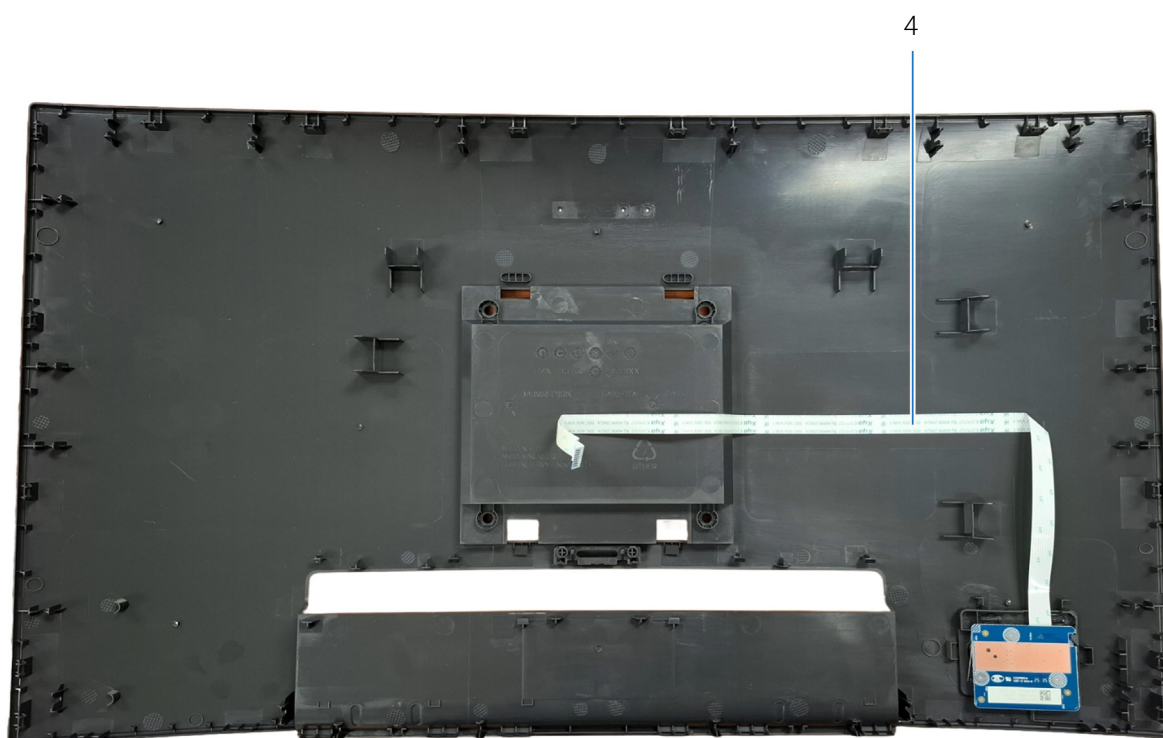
Conectividad de cables en la cubierta posterior de la pantalla
